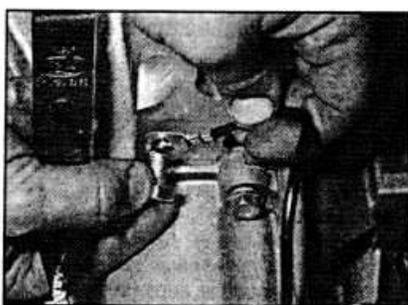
D.19. Болт крепления шины заземления к коробке передач.
